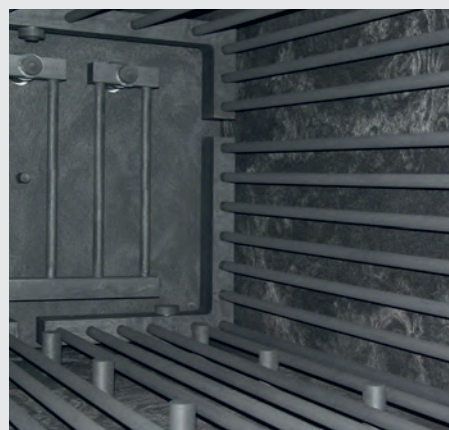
Рабочая камера печи НТК 400, вид изнутри: кольцевой нагревательный элемент и графитовые опоры для установки реторты, облегчающие загрузку и разгрузку печи
